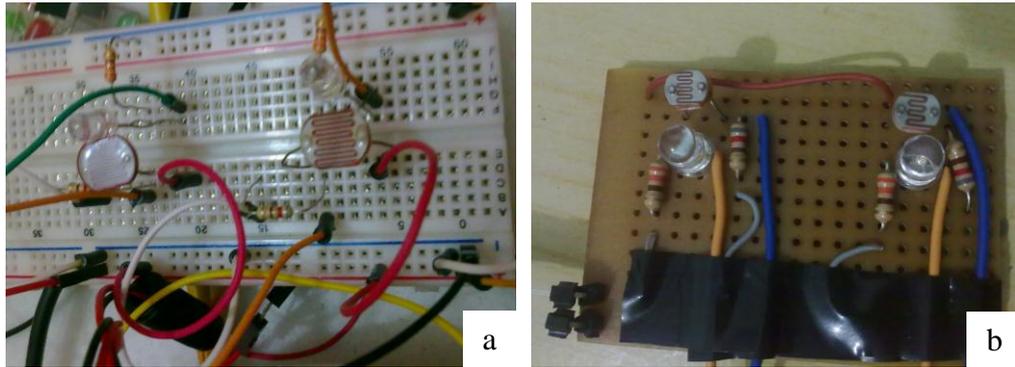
Montagem do sensor em uma Protoboard (a), Sensor soldado em uma placa universal para fixação no chassi (b).
